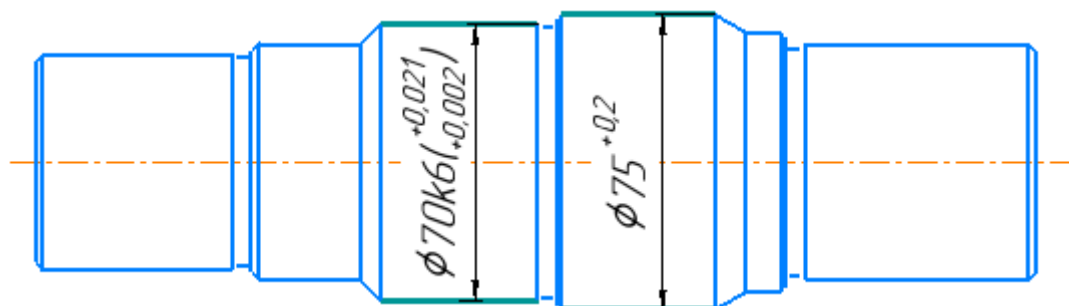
Эскиз с предполагаемыми поверхностями захвата
